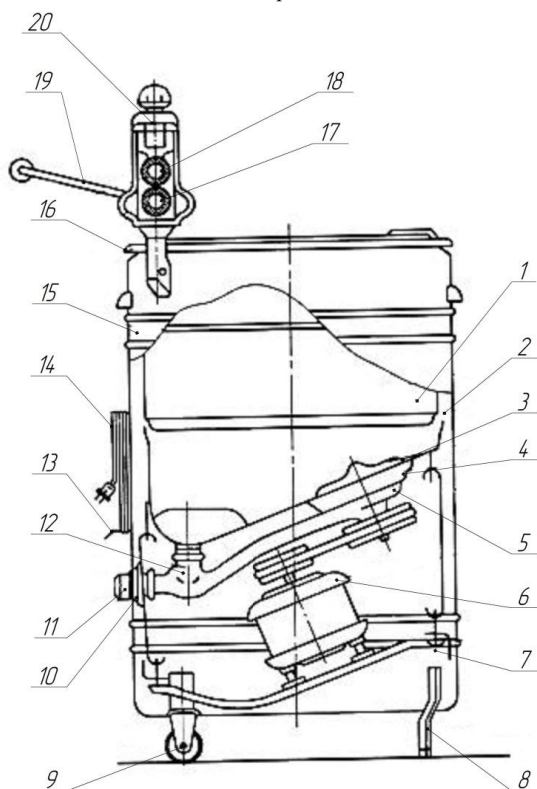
Будова машини активаторного типу: 1 – бак; 2 – корпус; 3 – активатор; 4 – відцентровий насос; 5 – зливний шланг; 6 – електродвигун; 7 – рама для кріплення двигуна; 8 – скоба; 9 – ролик; 10 – патрубок; 11 – пробка; 12 – шланг; 13 – скоба для намотування шнура; 14 – шнур; 15 – показчик рівня рідини; 16 – кришка; 17 – віджимні валики; 18 – знімна рукоятка; 19 – пружина; 20 – регулювальний гвинт.
